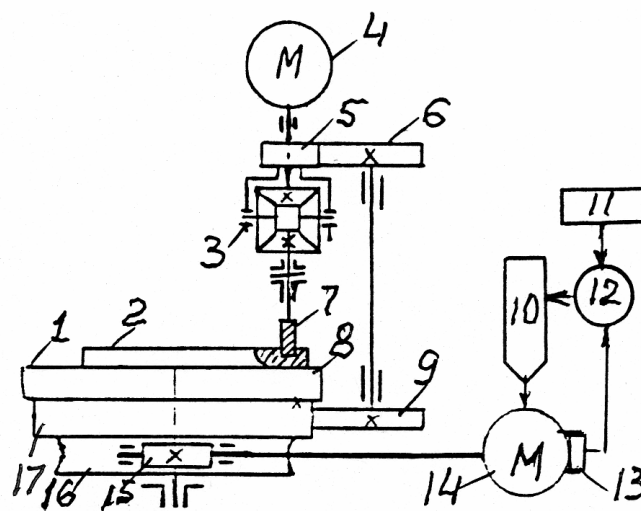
Схема приводу кругової подачі копіювально-фрезерного верстата
